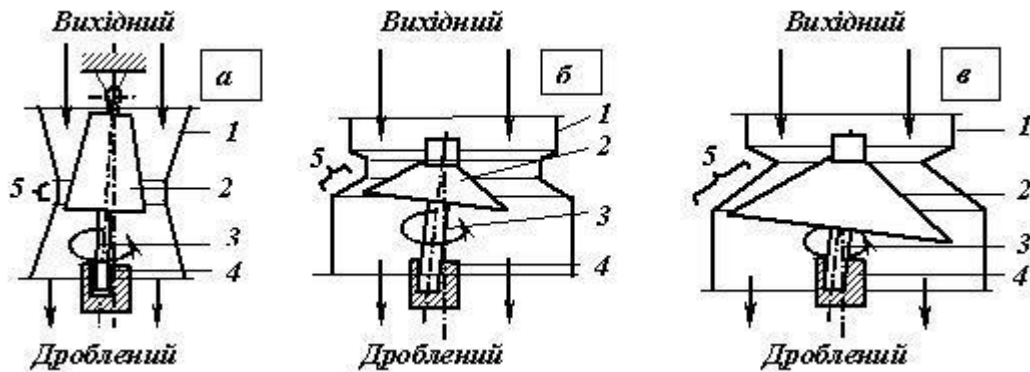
Схеми конусних дробарок: а — крупного дроблення; б — середнього дроблення; в — дрібного дроблення. 1 — конічна нерухома чаша; 2 — подрібнюючий конус; 3 — вал; 4 — ексцентриковий стакан; 5 — зона дроблення
